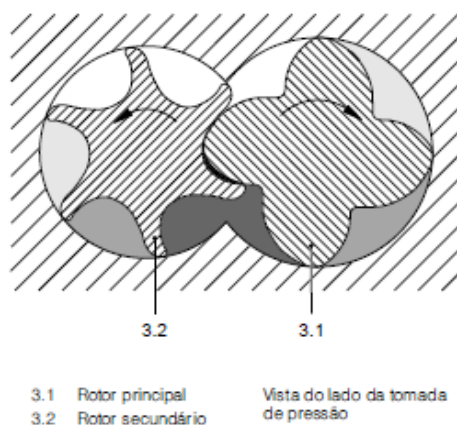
Perfil da engrenagem do motor (manual do fabricante).
